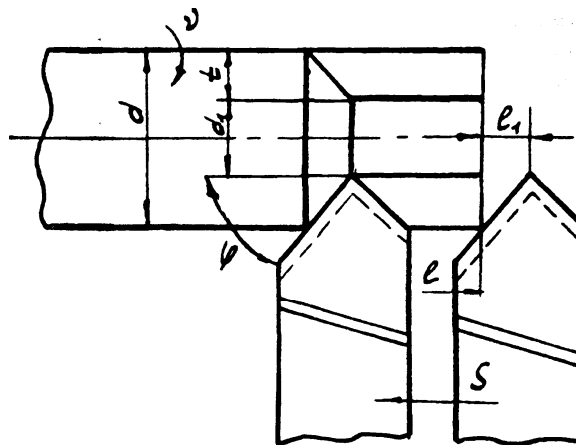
Схема обточения зовнішніх циліндричних поверхонь на токарно-му верстаті
